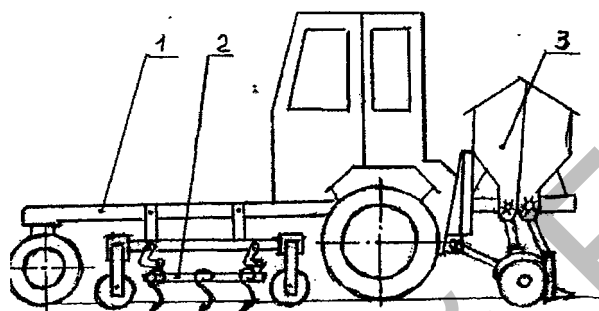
Схема почвообрабатывающего посевного агрегата:
